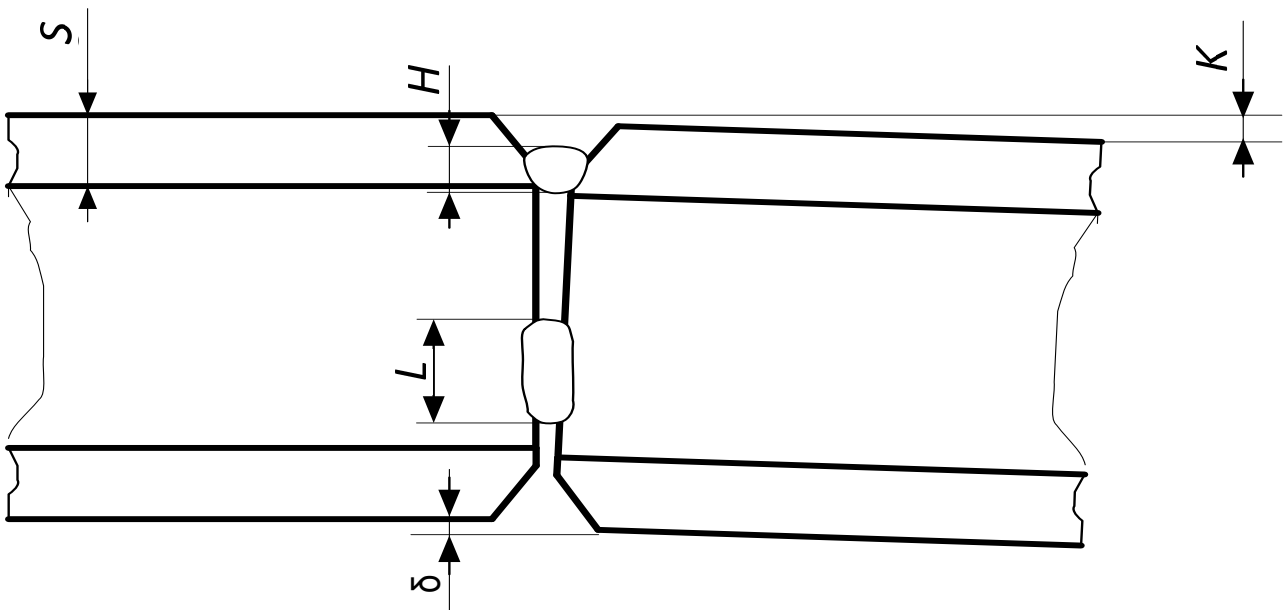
Эскиз контролируемого изделия при контроле сборки деталей под сварку (трубы)
